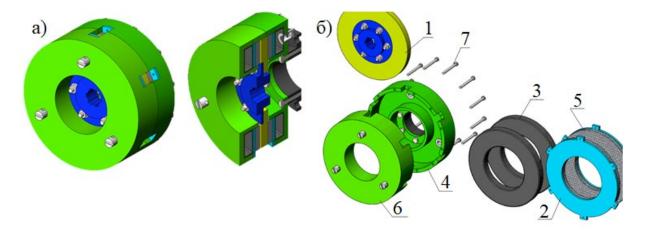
Дисковый тормозной механизм с пневматическим приводом и кольцевыми тормозными колодками: а – дисковый тормозной механизм в сборе; б – дисковый тормозной механизм, разнесенный по деталям; 1 – тормозной диск; 2 – тормозная колодка; 3 – тороидальная камера; 4 – внутренняя часть корпуса; 5 – кольцевая фрикционная накладка; 6 – внешняя часть корпуса; 7 – болт
